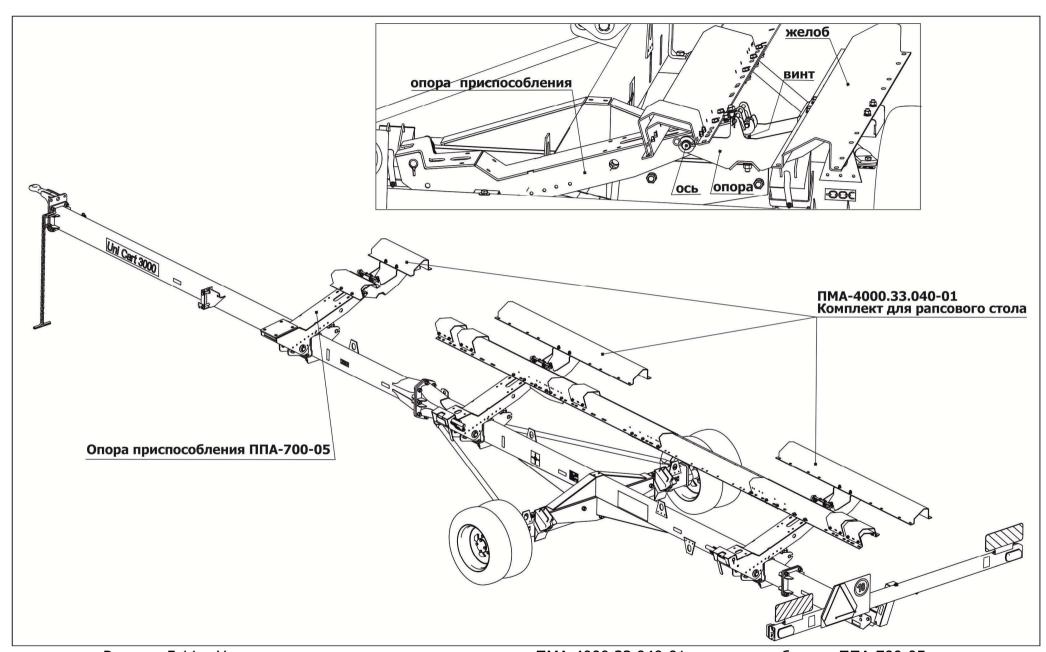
Установка комплекта для рапсового стола ПМА-4000.33.040-01 на приспособление ППА-700-05
